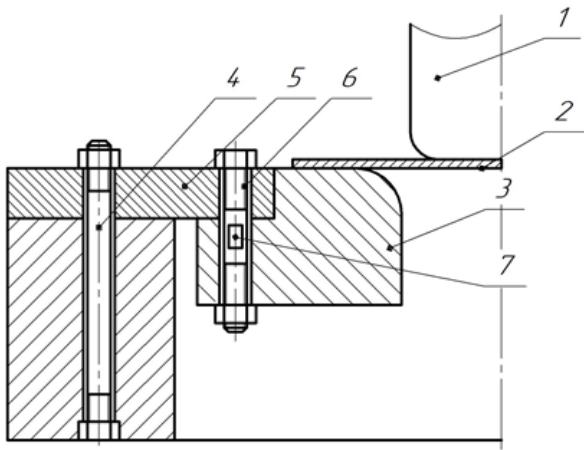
Оснащення для вимірювання напружень тертя на радіусі заокруглення витяжної матриці: 1 – пуансон; 2 – заготовка; 3 – рухома вставка; 4 – кріпильний болт; 5 – сполучне кільце; 6 – месдоза; 7 – тензорезистор
